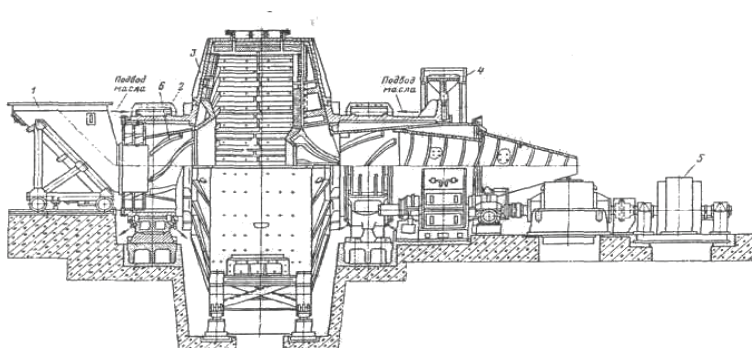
Мельница для мокрого самоизмельчения: 1 - откатная загрузочная воронка; 2 - подшипник; 3 - корпус мельницы; 4 - зубчатый венец привода; 5 - электродвигатель; 6 - спираль подачи пульпы
